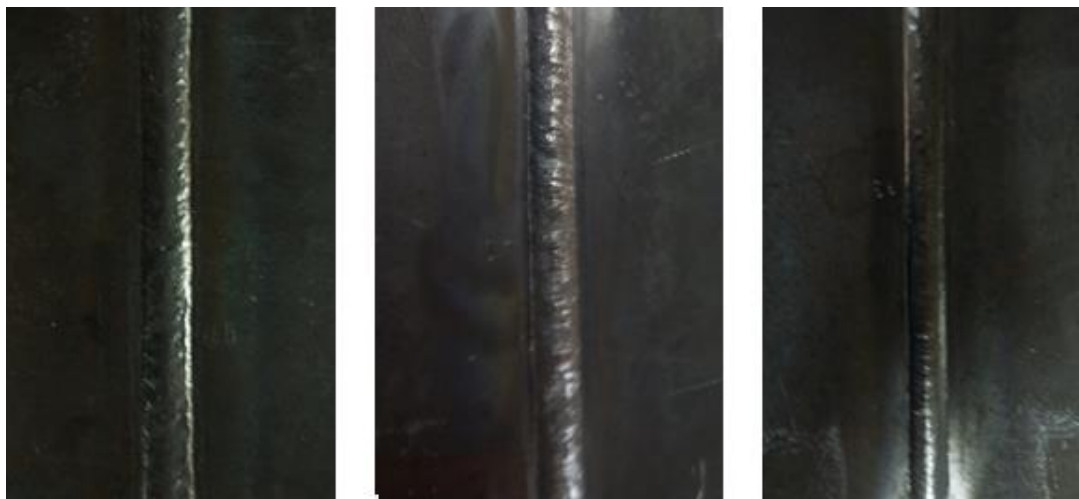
Limpieza de los cordones luego de la soldadura
